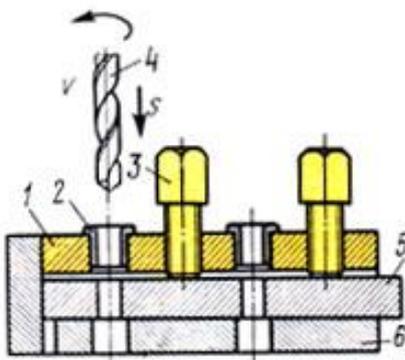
Накладной кондуктор: 1 - крышка, 2 - втулка, 3 - винты, 4 - сверло, 5 - деталь, 6 - основание
